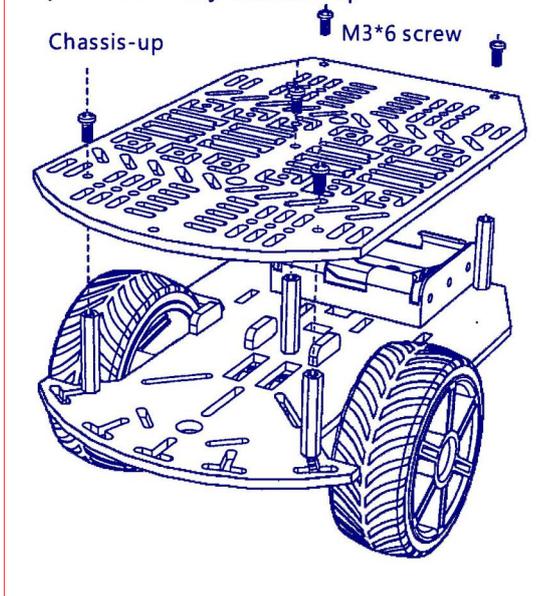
ASSEMBLAGGIO FINALE DELLO CHASSIS
